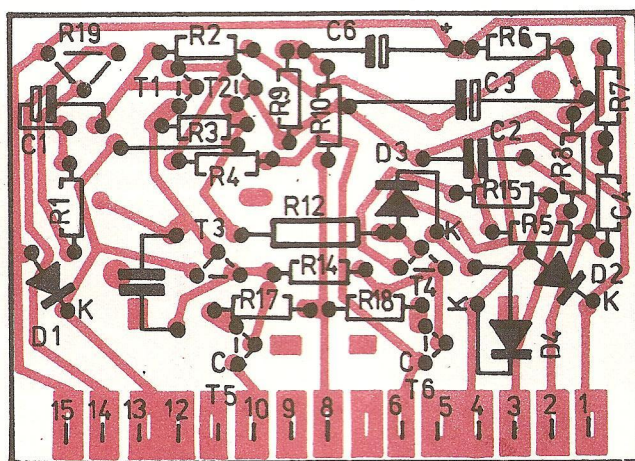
Deska elektronické pojistky 3AK 060 49 (strana součástek)
